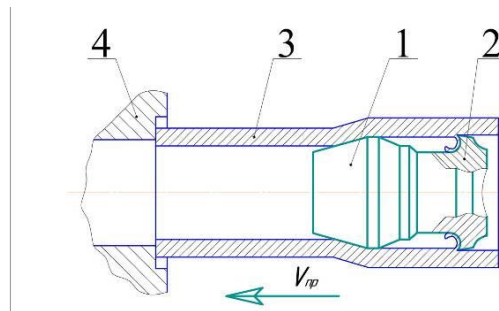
Схема обробки: 1- деформувальний елемент; 2- різальний зубець; 3- деталь; 4- опора.
